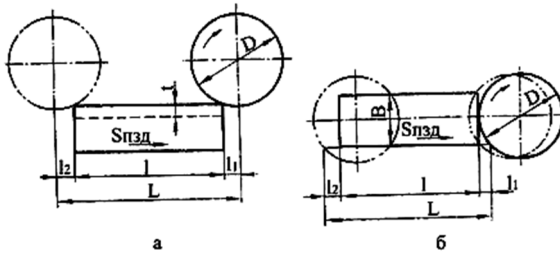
Схема визначення розрахункової довжини заготовки при фрезеруванні циліндричною (а) і торцевою (б) фрезами
